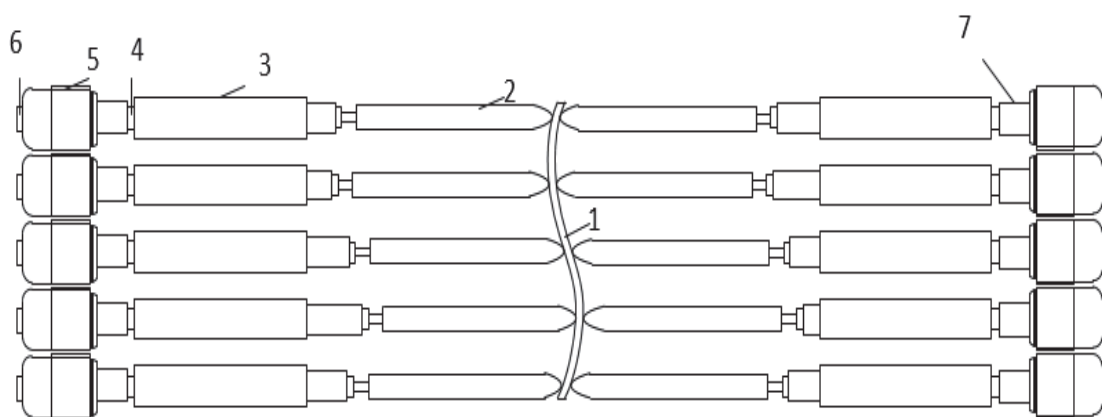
Схематичное расположение формирующих стержней: 1 – заготовка; 2 – стержень; 3 – актуатор; 4 – датчик положения; 5 – двигатель; 6 – датчик скорости; 7 – редуктор
